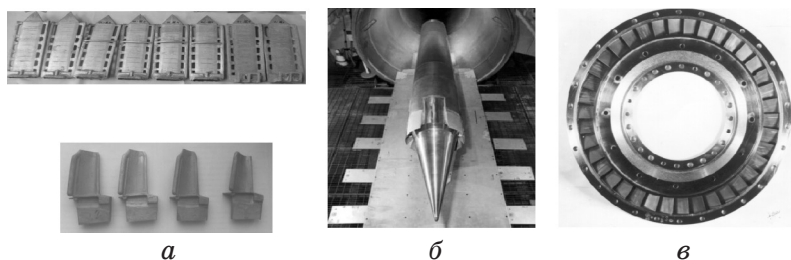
Проставки реактивного сопла и отливки рабочих неохлаждаемых лопаток из сплава ВКНА-1В на основе Ni3Al (а); фрагмент ГПВРД с деталями из NiAl-Y₂O₃ (б) и сопловой аппарат с НР лопатками из NiAl-Y₂O₃ (в) алюминидов никеля.
